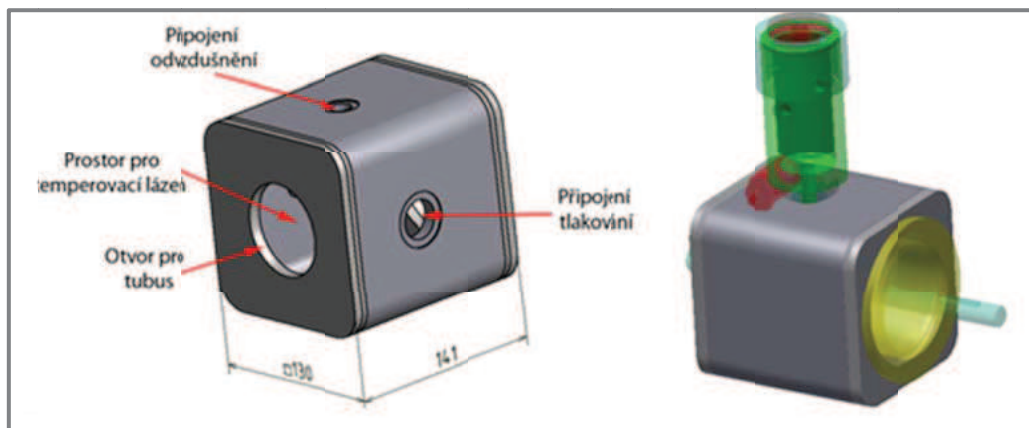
Varianta 2 tlakovací části konstrukce
